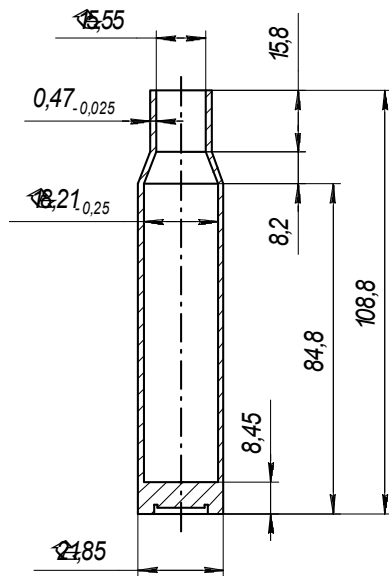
Эскиз штампуемой детали с размерами
